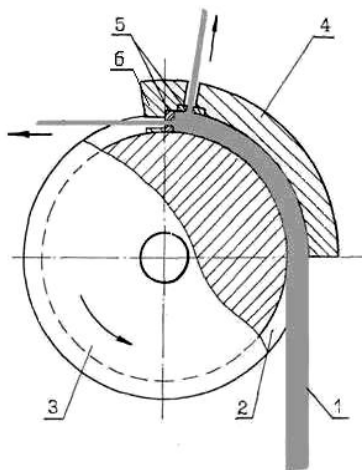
Схема устройства для непрерывного прессования с горизонтальной осью вращения колеса: 1 – заготовка; 2 – ручей; 3 – вращающееся колесо; 4 – матрицедержатель; 5 – матрицы, 6 – упор
